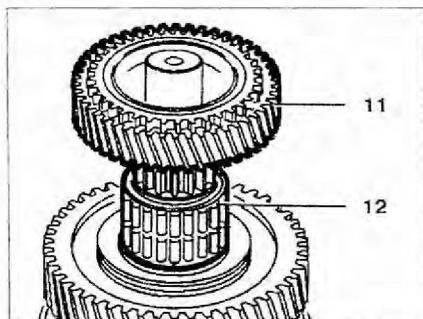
Снимите шестерню 11 3-й передачи и игольчатый подшипник 12.
